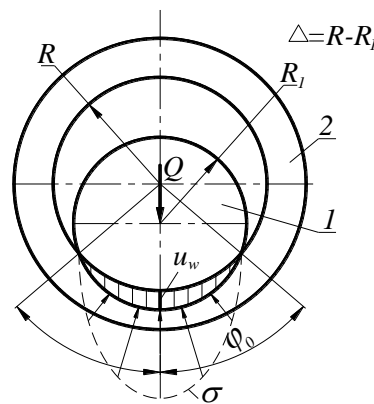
Розрахункова схема циліндричного підшипника ковзання
